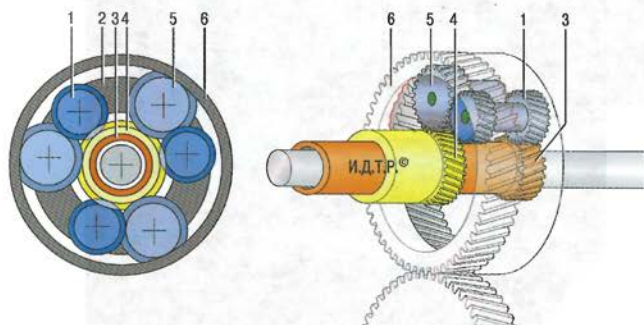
Планетарный редуктор системы Равинь: 1 – длинный сателлит; 2 – водило; 3 – малая солнечная шестерня; 4 – большая солнечная шестерня; 5 – короткий сателлит; 6 – коронная шестерня
